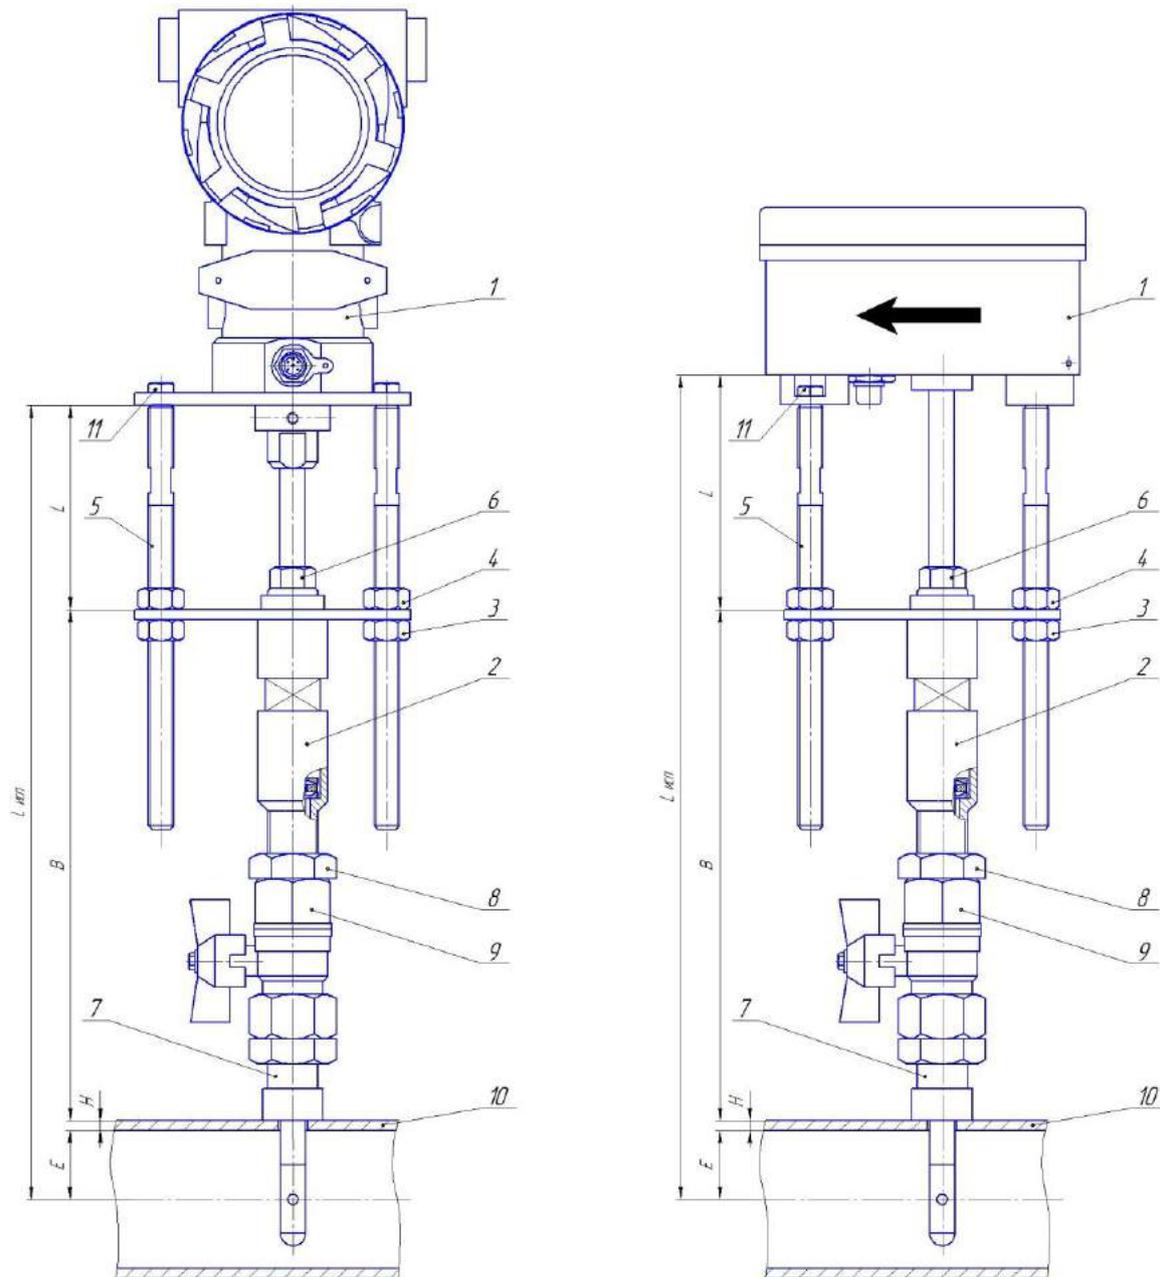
Монтаж расходомера РС-2М на стальную трубу
